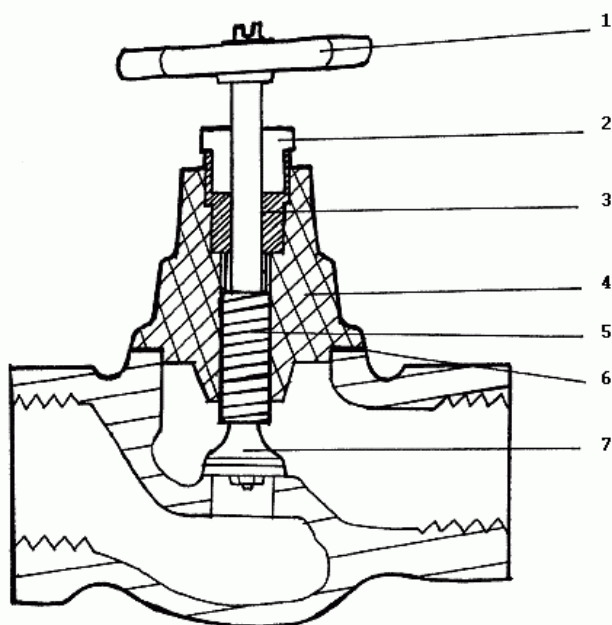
Устройство вентилей: 1 – маховик; 2 – втулка; 3 – набивка сальника; 4 – корпус головки; 5 – резьба штока; 6 – изоляция; 7 – клапан с прокладкой
